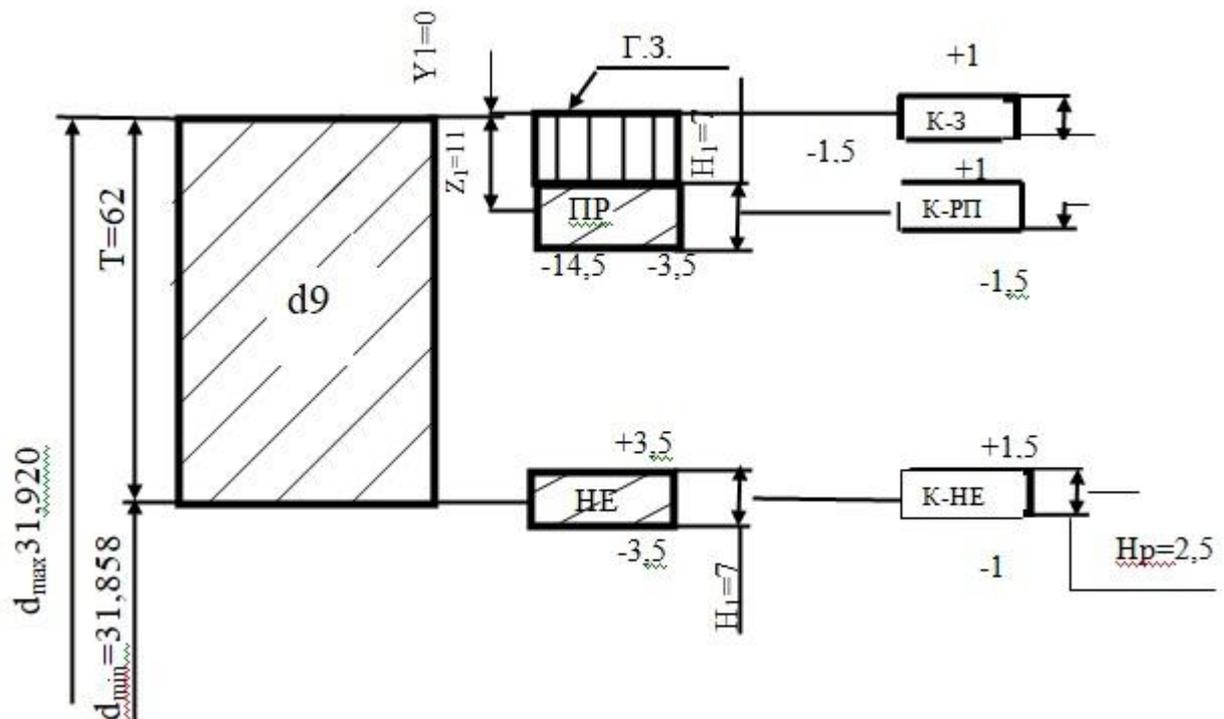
Схема розміщення полів допусків калібр-скоби для контролю вала $\varnothing 32d9_{(-0,080)}^{(-0,142)}$
